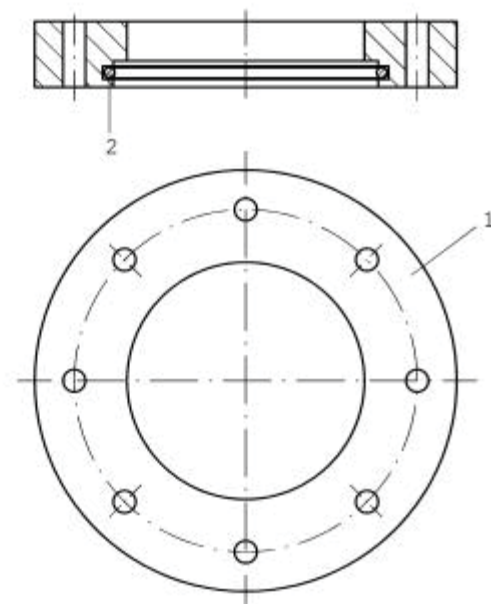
c: Flansch oben (1) inklusive O-Ring-Dichtung (2)
